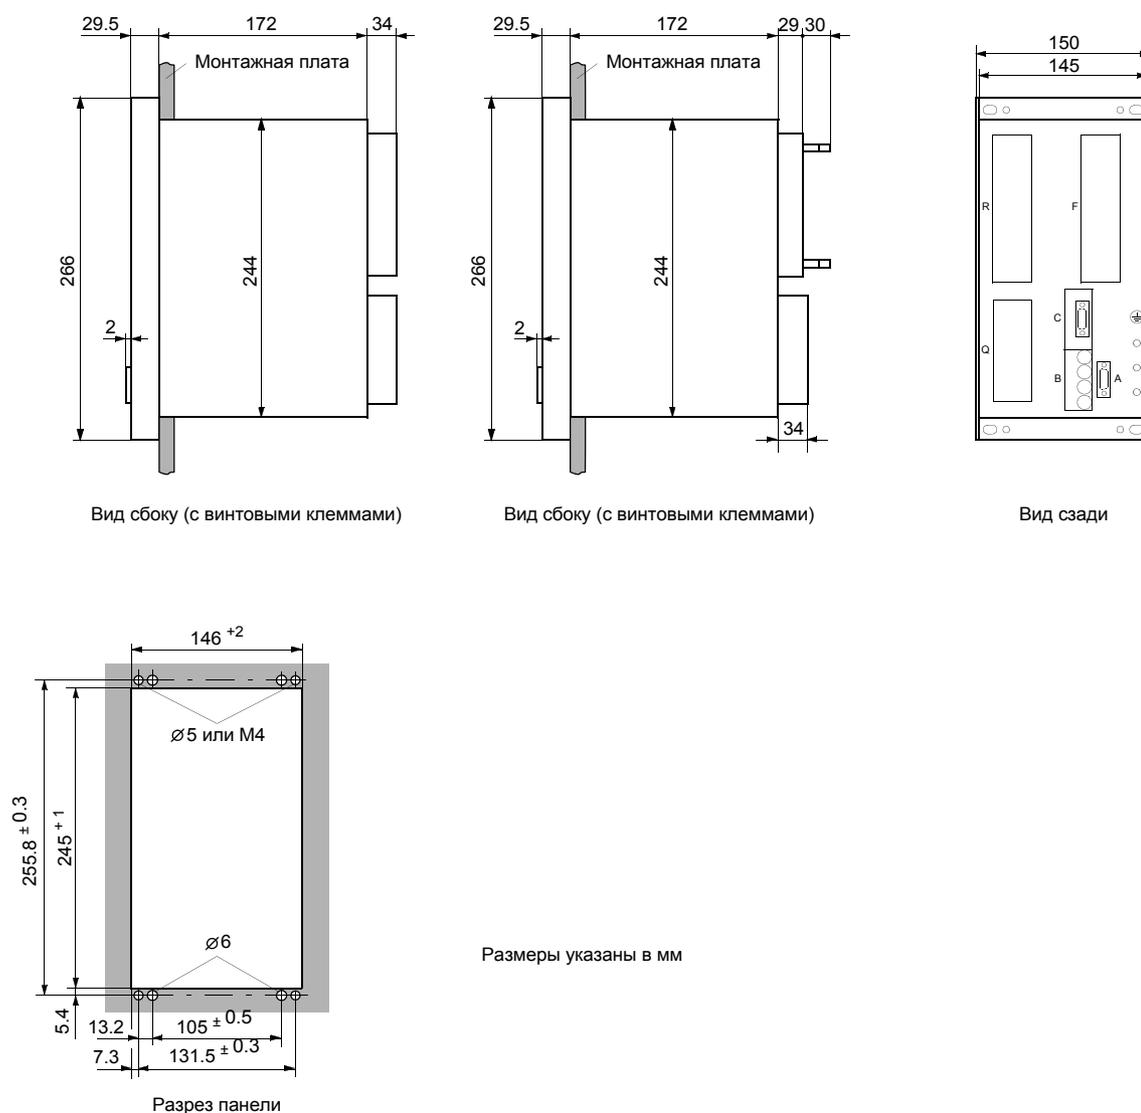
Размеры устройства 7UT612 с корпусом для утолщенного монтажа или монтажа в шкафу
